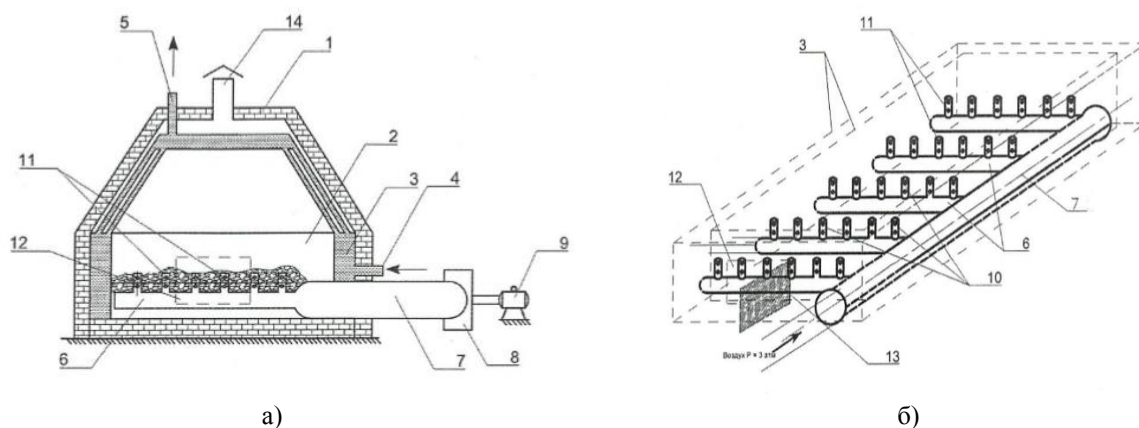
Вертикальный разрез котла (а) и размещение форсунок для подачи воздуха (б)
